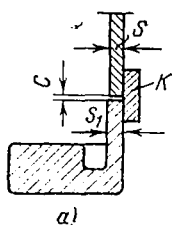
Сверхвысоковакуумное соединение фланца с трубой. Сварка на подкладке.
